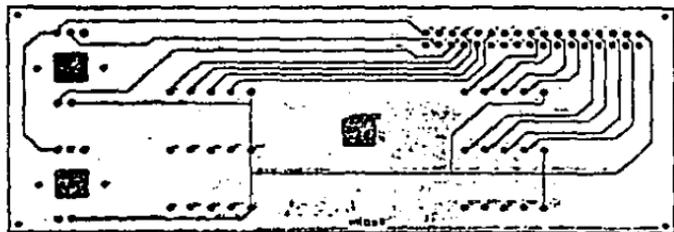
Circuito impreso "de interruptores" lado de componentes.
